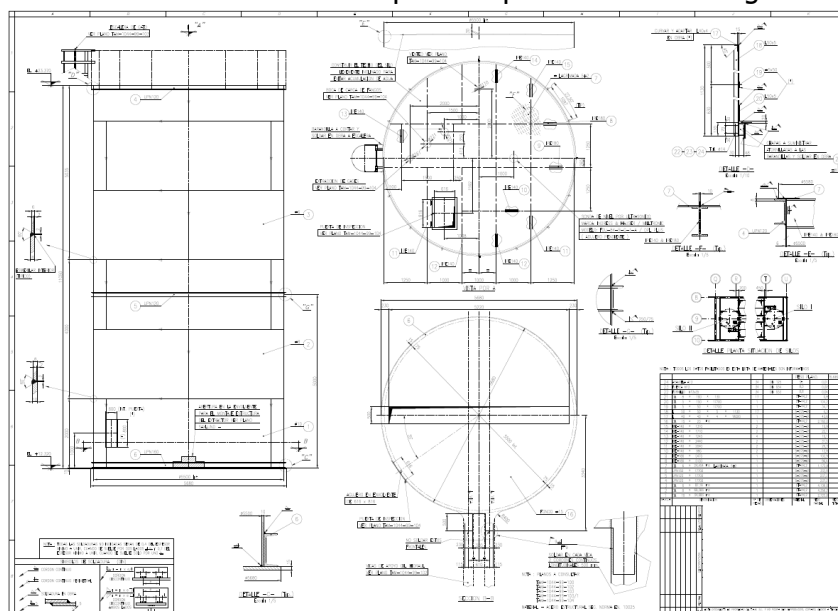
Ejemplo de plano de detalle con lista de materiales.
